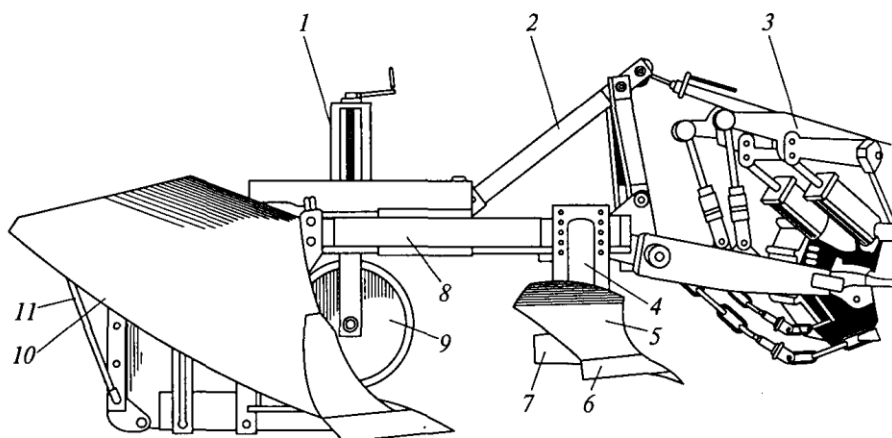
Плуг плантажный навесной ППН-50:
